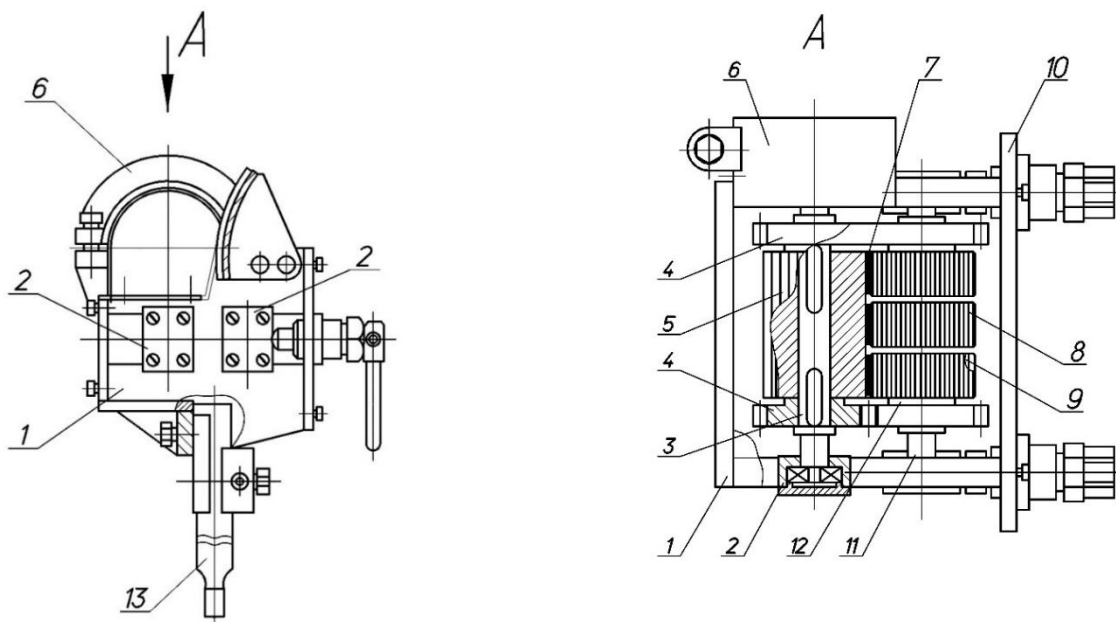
Приставка для наплавлення трьома стрічковими електродми
